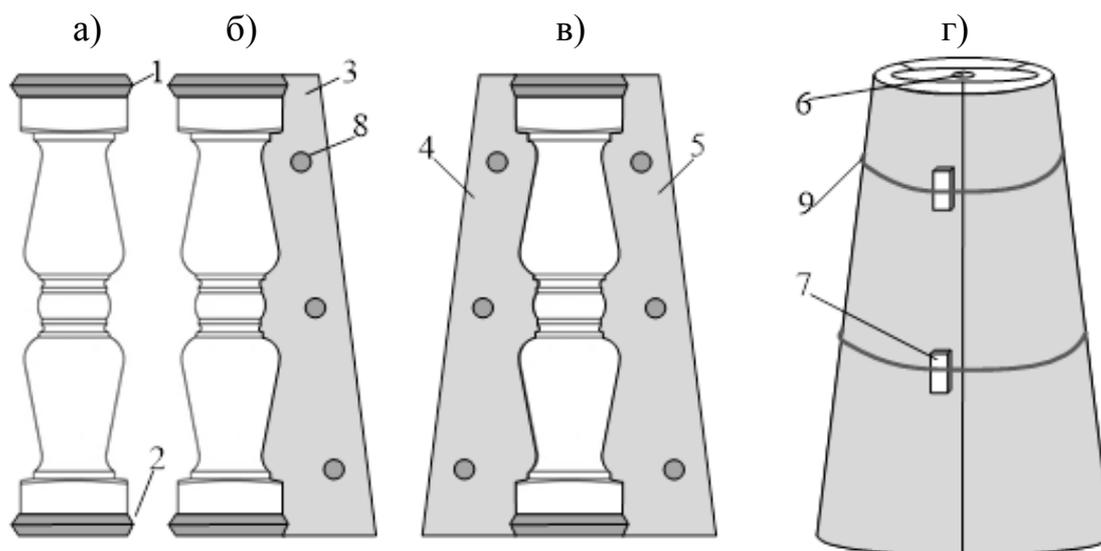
Изготовление формы балясины для отливки полых изделий:
